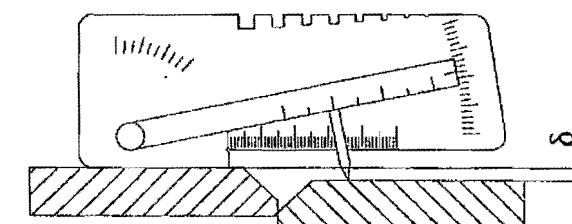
3. Схема измерений смещения поверхностей (δ) свариваемых или сваренных деталей
